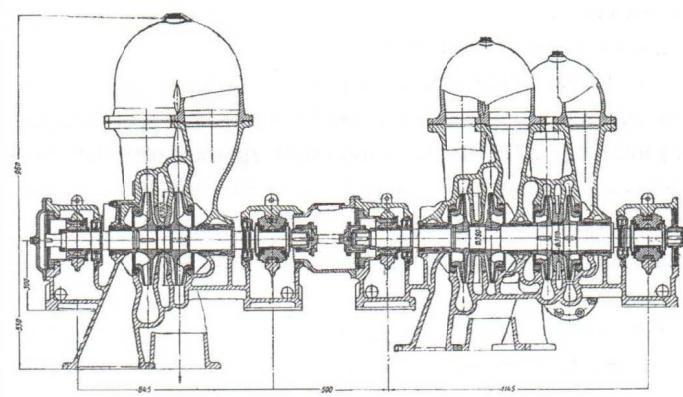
Компрессор типа ТК-8 конструкции ВНИИКИМАШ
